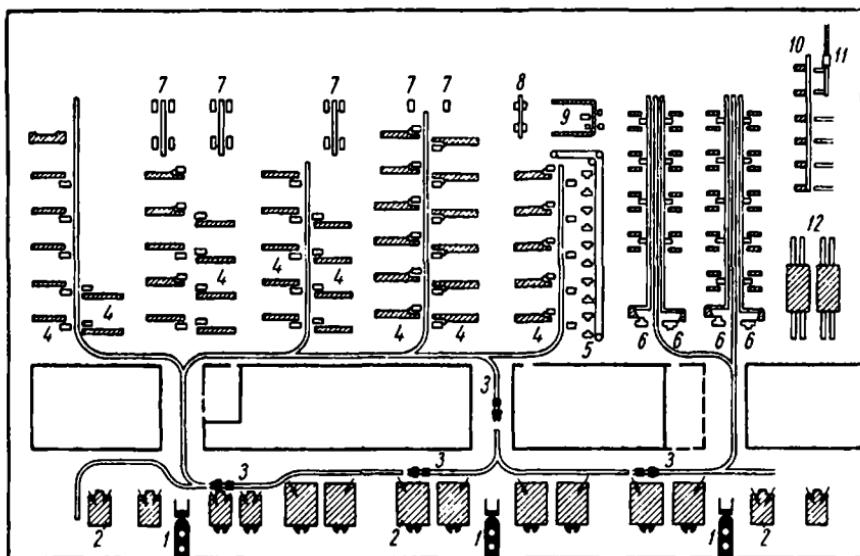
План крупного цеха литья в металлические формы и под давлением для изготовления автомобильных деталей:
